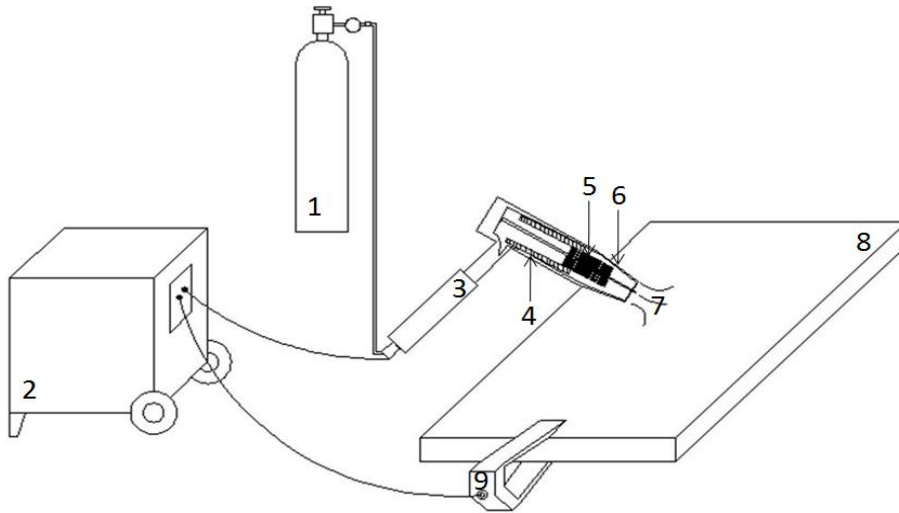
Equipamento para a refusão TIG: 1. Fornecimento de gás inerte; 2. Máquina de soldadura; 3. Porta-eléctrodo; 4. Condutor eléctrico; 5. Isolante (insulating heath); 6. Passagem de gás; 7. Gás de protecção; 8. Objecto a soldar; 9. Linha de terra
